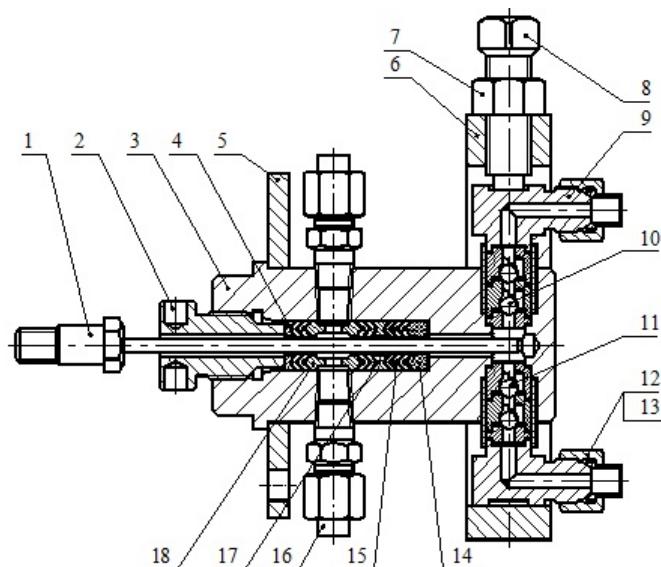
Гидроцилиндр: 1 – плунжер; 2 – стакан нажимной; 3 – цилиндр; 4 – кольцо нажимное; 5 – фланец цилиндра; 6 – хомут; 7 – гайка; 8 – винт; 9 – штуцер клапана; 10 – нагнетательный клапан; 11 – всасывающий клапан; 12 – ниппель; 13 – гайка накидная; 14 – грунтовка; 15 – манжета; 16 – штуцер промывочный; 17 – кольцо; 18 – фонарь
